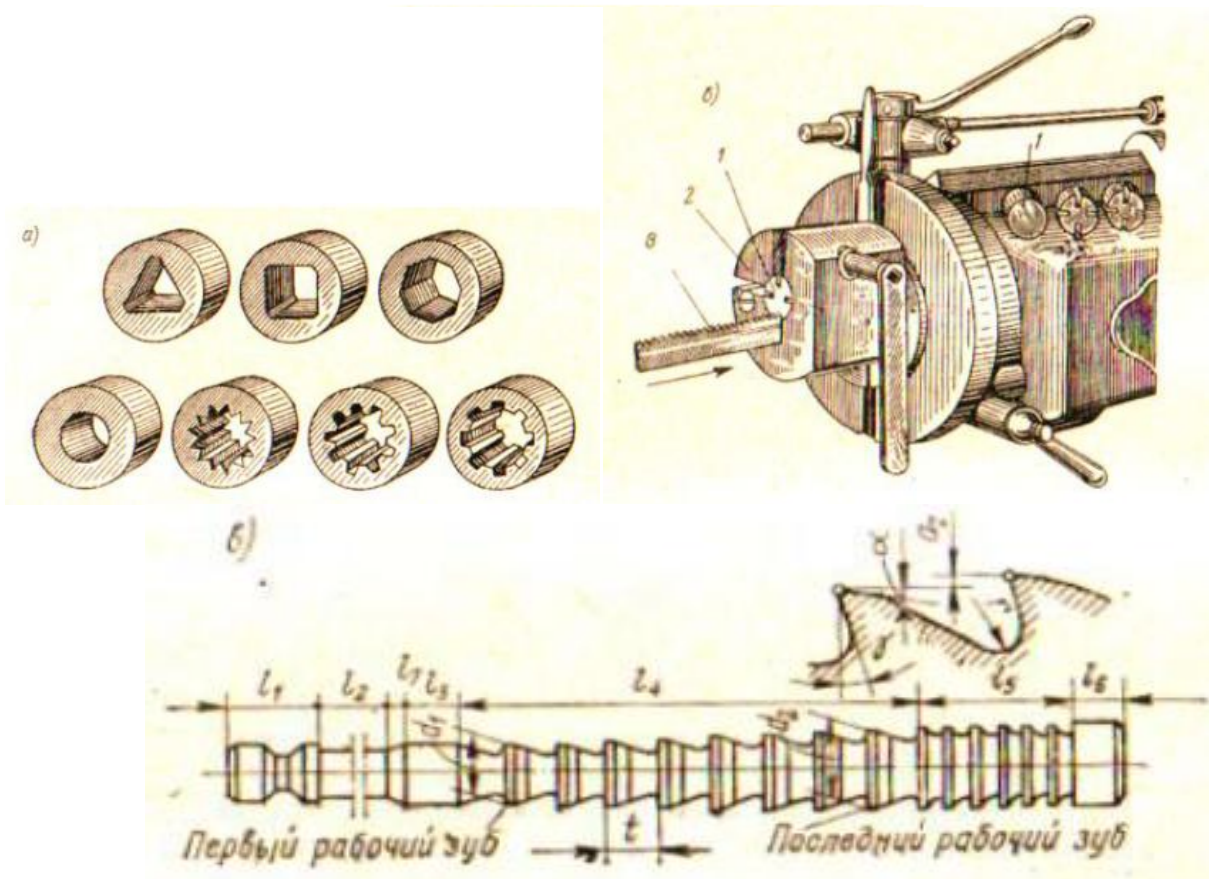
Протягивание деталей: а) формы поверхностей, обрабатываемых внутренним протягиванием; б) протягивание пазов шпоночной протяжкой; в) элементы и геометрические параметры режущей части круглой протяжки (в мм):  $l_1$  - длина хвоста;  $l_2$  - длина шейки;  $l_3$  - длина переднего направления;  $l_4$  - длина режущей части;  $l_5$  - длина калибрующей части;  $l_6$  - длина концевой части;  $l_7$  - длина переходного конуса;  $t$  - шаг зубьев протяжки;  $r$  - радиус закругления у основания зуба;  $\alpha$  - задний угол зуба протяжки;  $\gamma$  - передний угол
